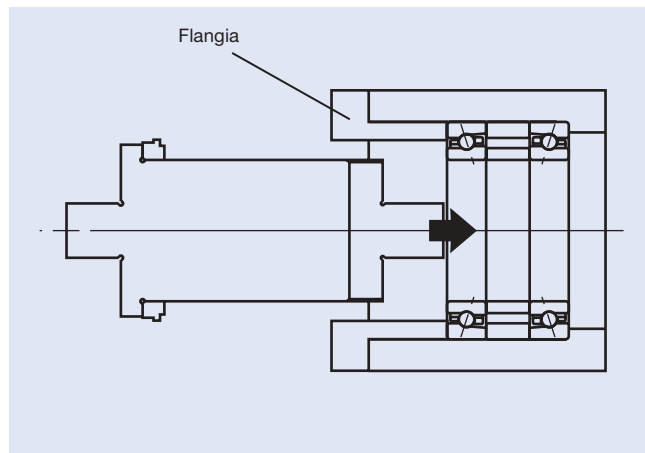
Montaggio con Disposizione Faccia a Faccia
